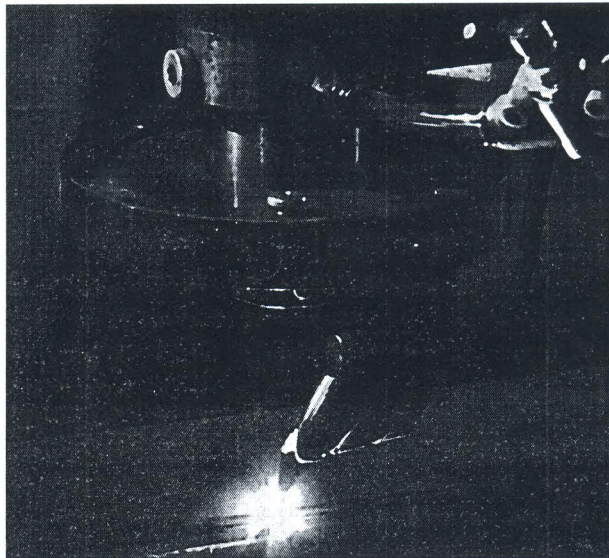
Процесс лазерной сварки Al-Li сплава 3 поколения (ИПТМ СО РАН).
